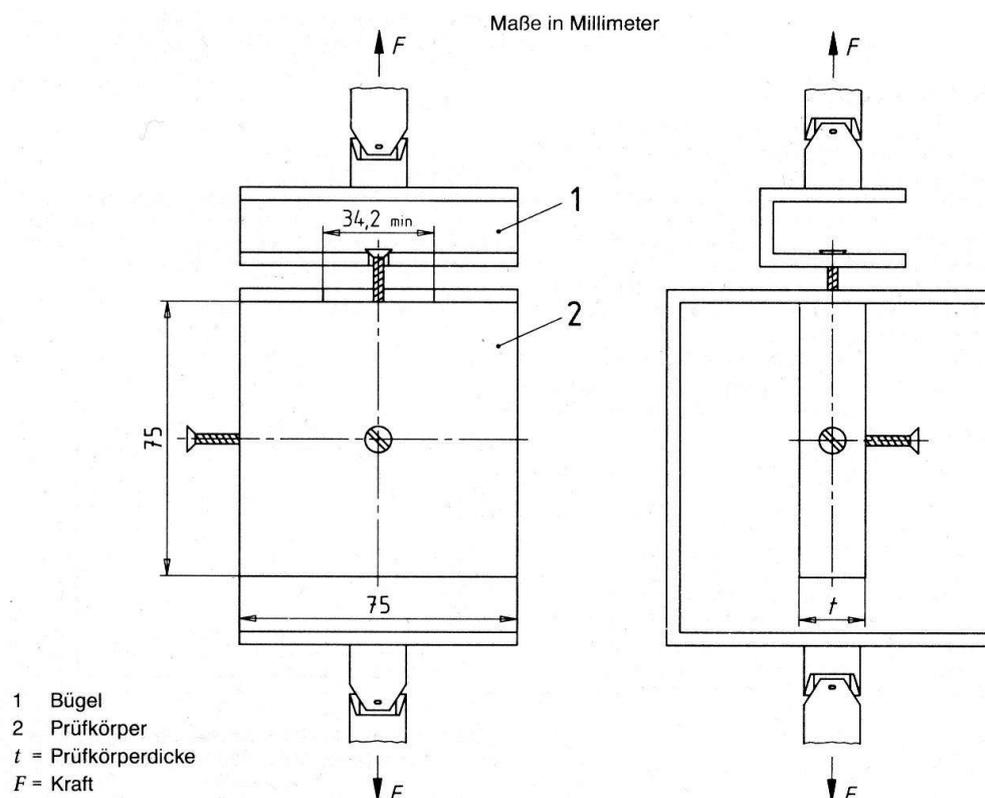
Prinzip der Schraubenauszugsprüfung gemäß EN 320
